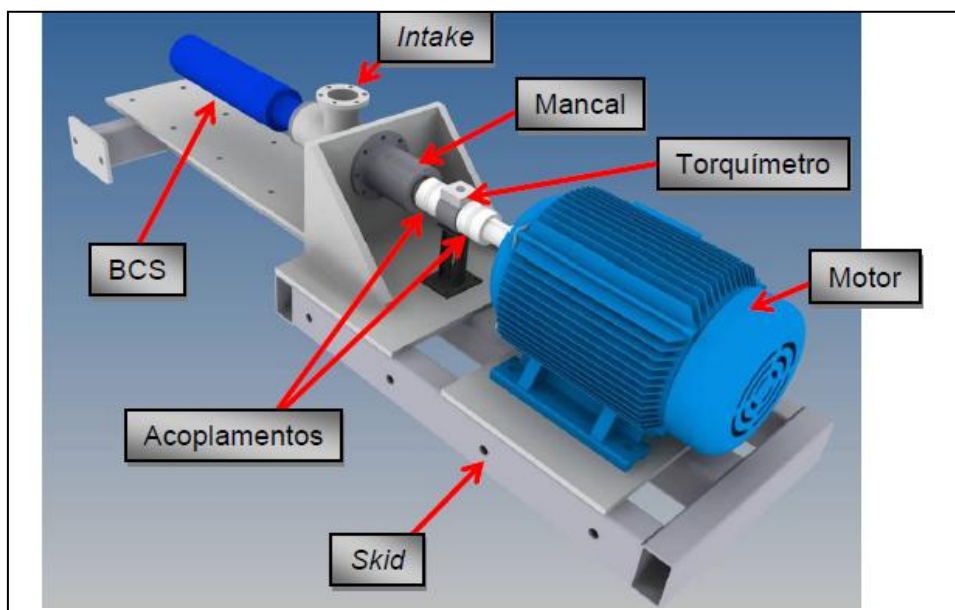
Esquema de montagem do skid com os principais componentes.
